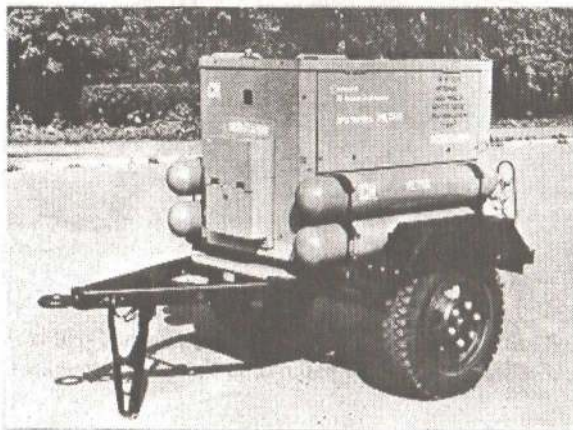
Общий вид сварочной установки АДД-4002У1 с системой питания, модернизированной для работы на сжатом природном газе
